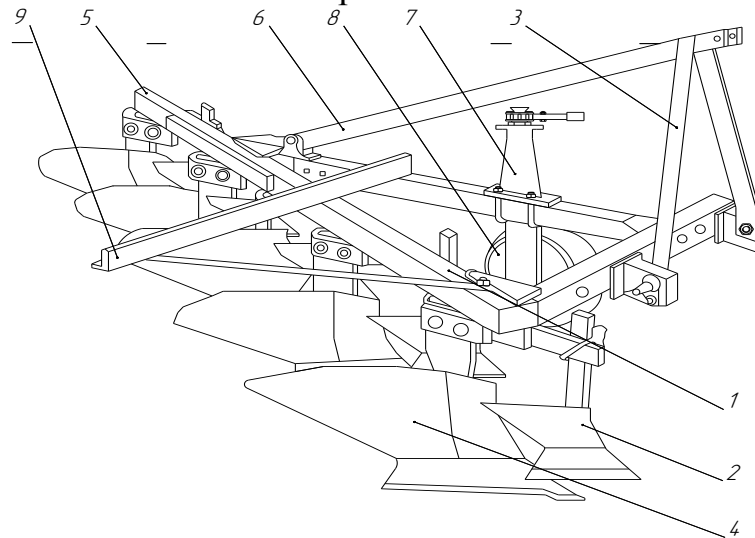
Плуг лемішний начіпний п'ятикорпусний ПЛН-5-35:
